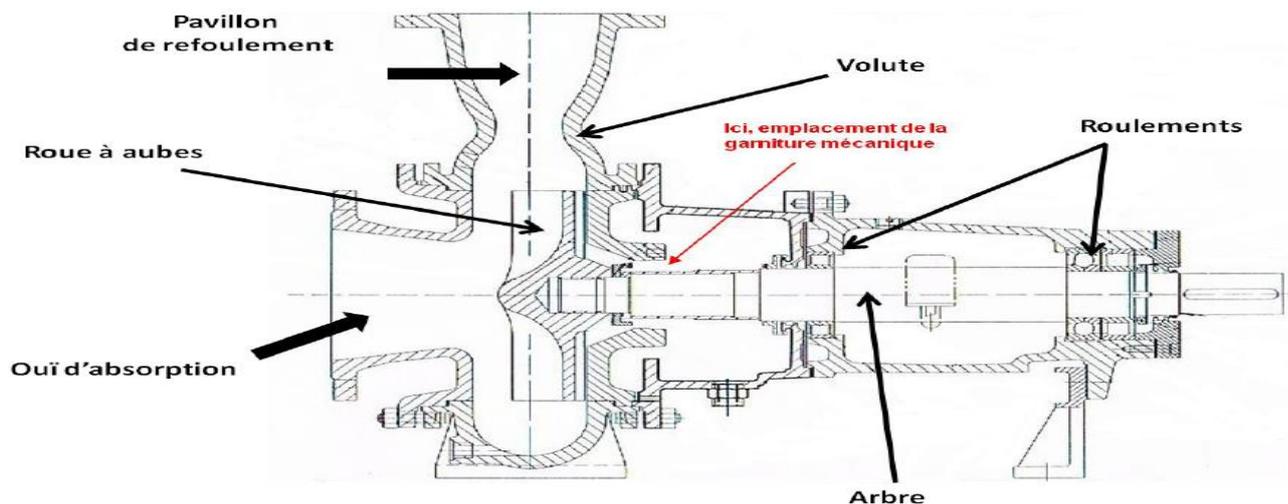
dessin d'ensemble en vue de coupe de la pompe centrifuge à bouillie
